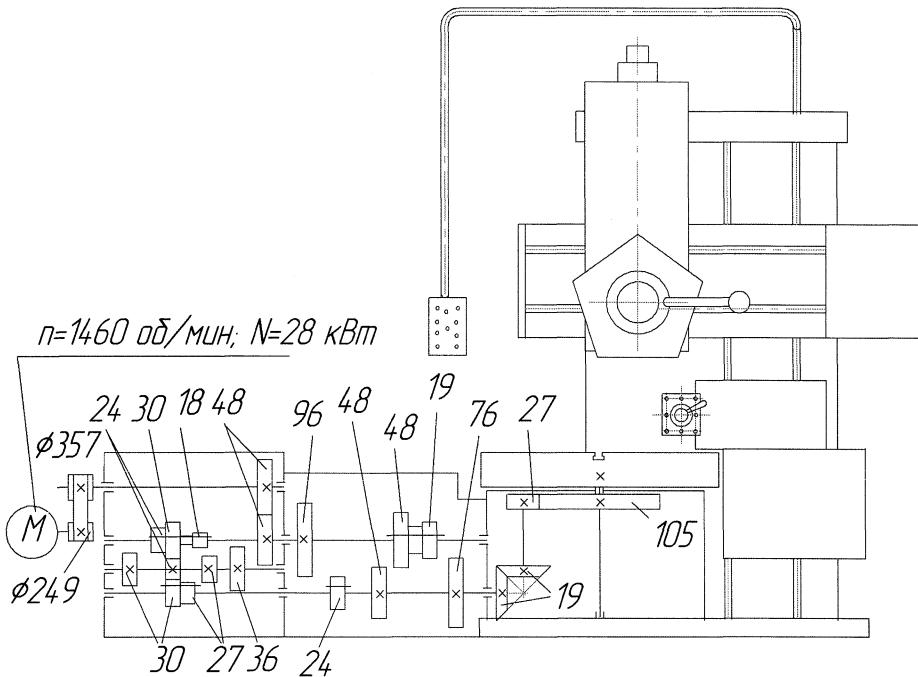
Кинематическая схема коробки скоростей станка 1531Б
